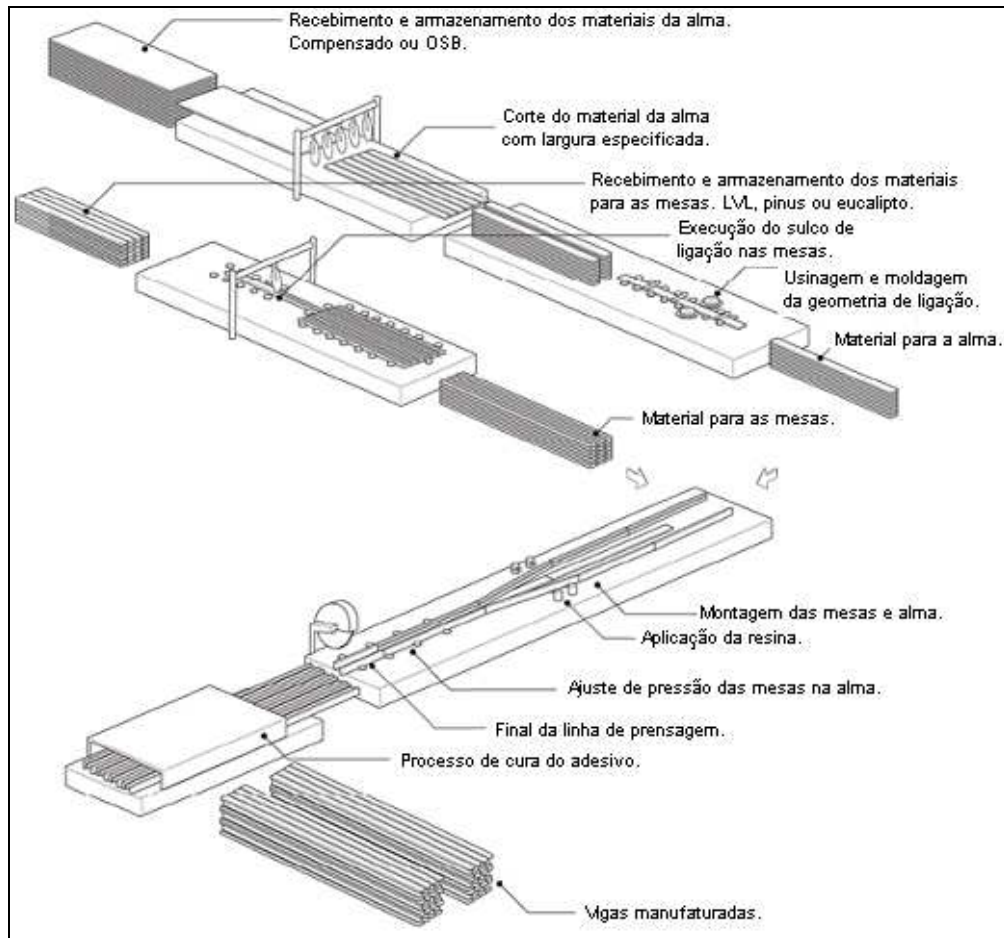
Modelo de fabricação de vigas em perfil "I"
